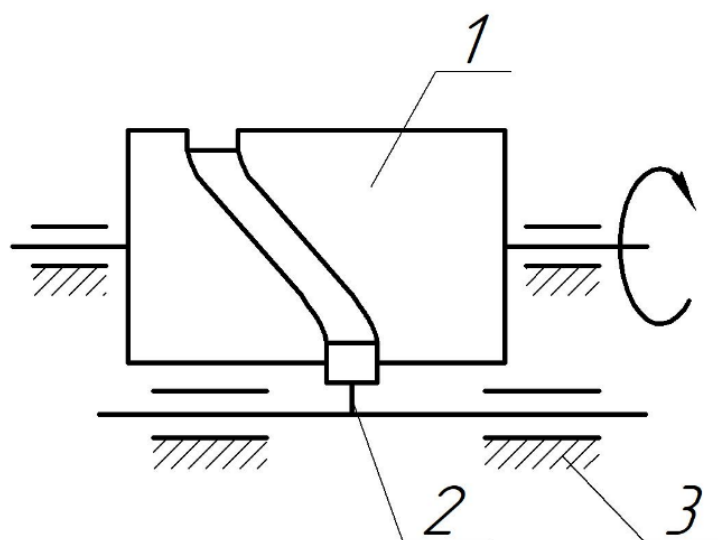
Пространственный цилиндрический кулачковый механизм
